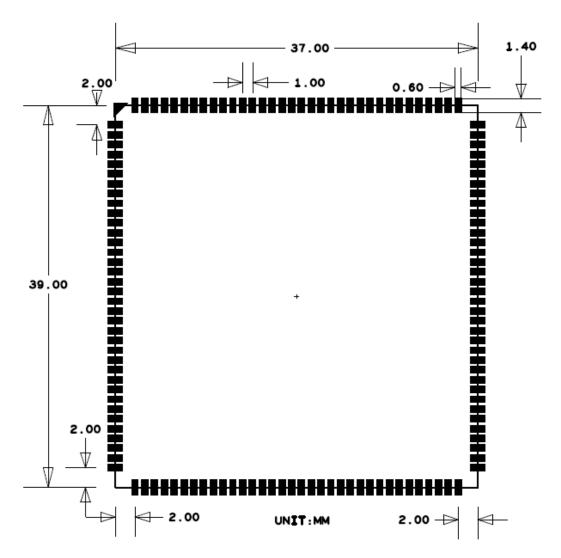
MYC-Y6ULX 推荐 PCB 封装
